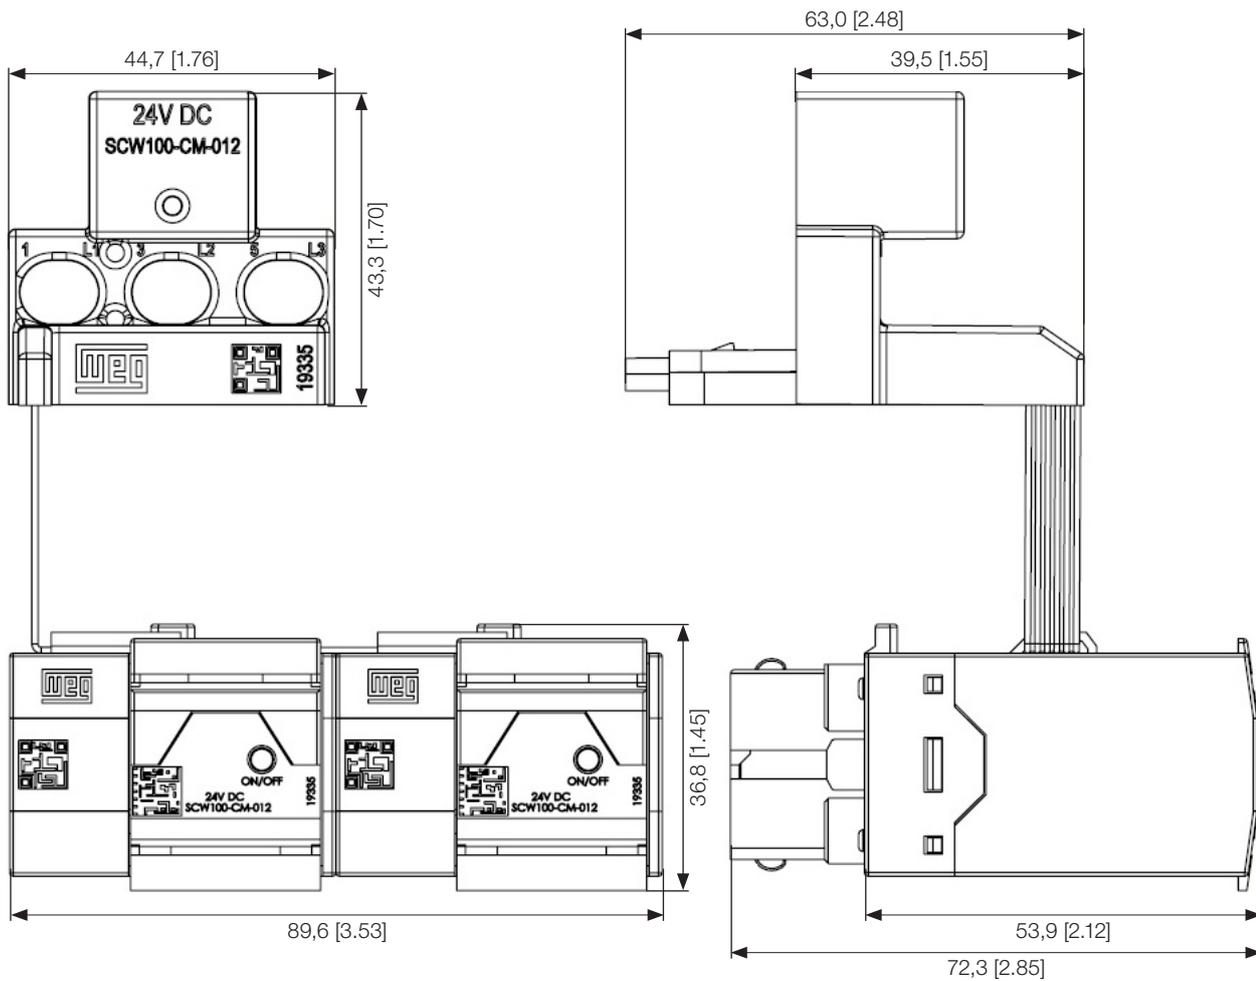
Dimensões do Módulo de Conexão Partida Reversora com disjuntor-motor (CM-012) em mm [in]
